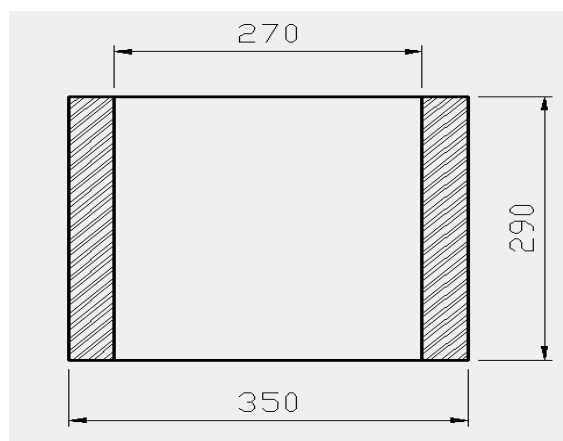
ESQUEMA DE LAS DIMENSIONES DEL BOCÍN.
